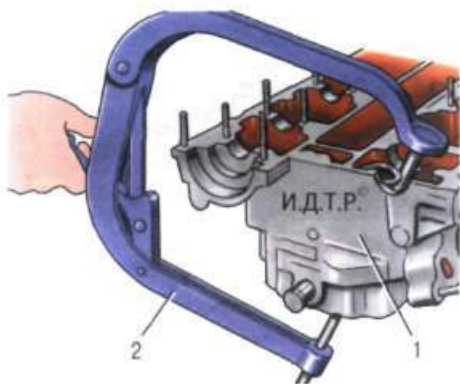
Установка приспособления для сжатия пружин клапанов: 1 – головка блока цилиндров; 2 – приспособление для сжатия пружин
